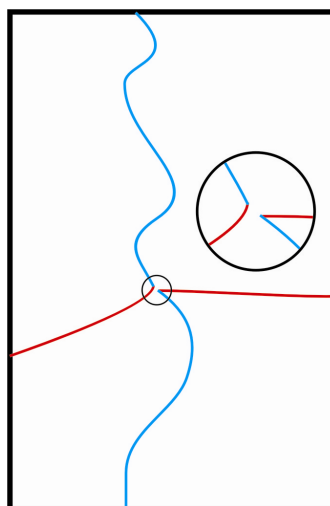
Ejemplo de corte interrumpido y grietas indeseadas
